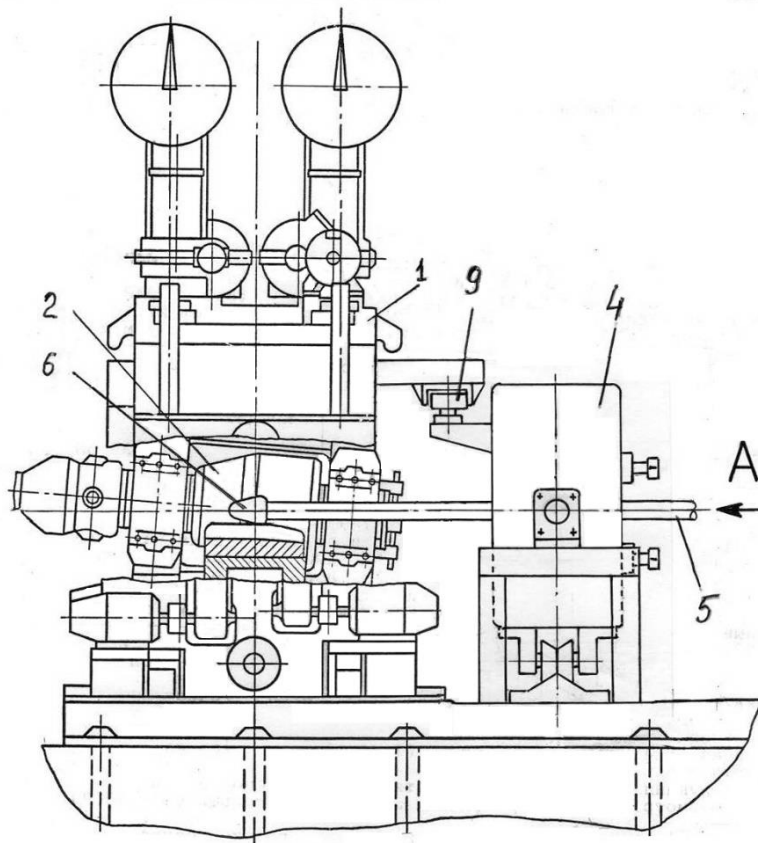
Загальний вид кліті прошивного стана і обкатного пристрою
